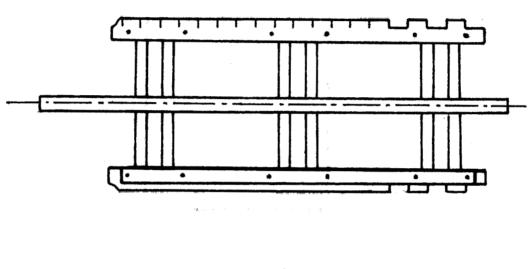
VISTA EN CONJUNTO DEL ROTOR IMPACTADOR.
